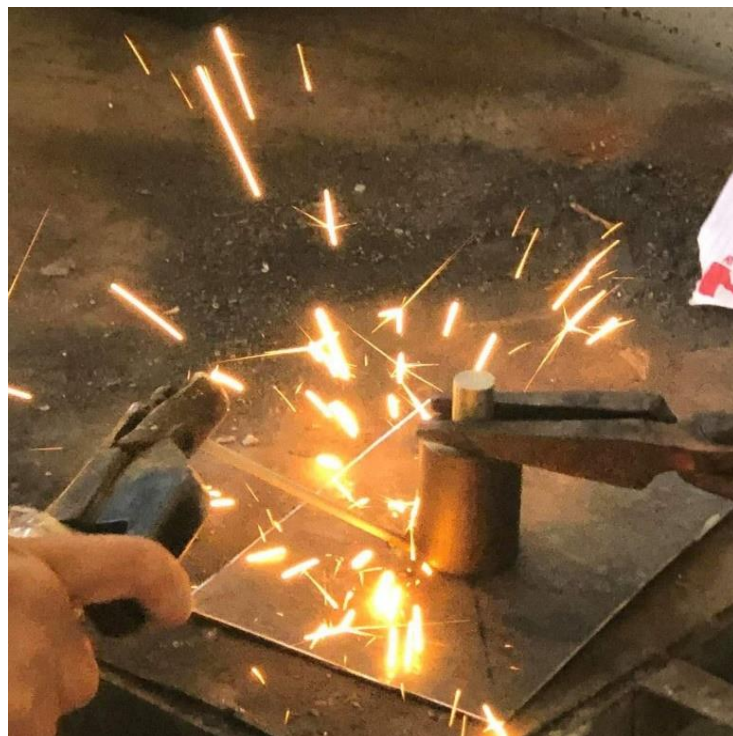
Soudage de la pièce 1 sur la plaque métallique.
